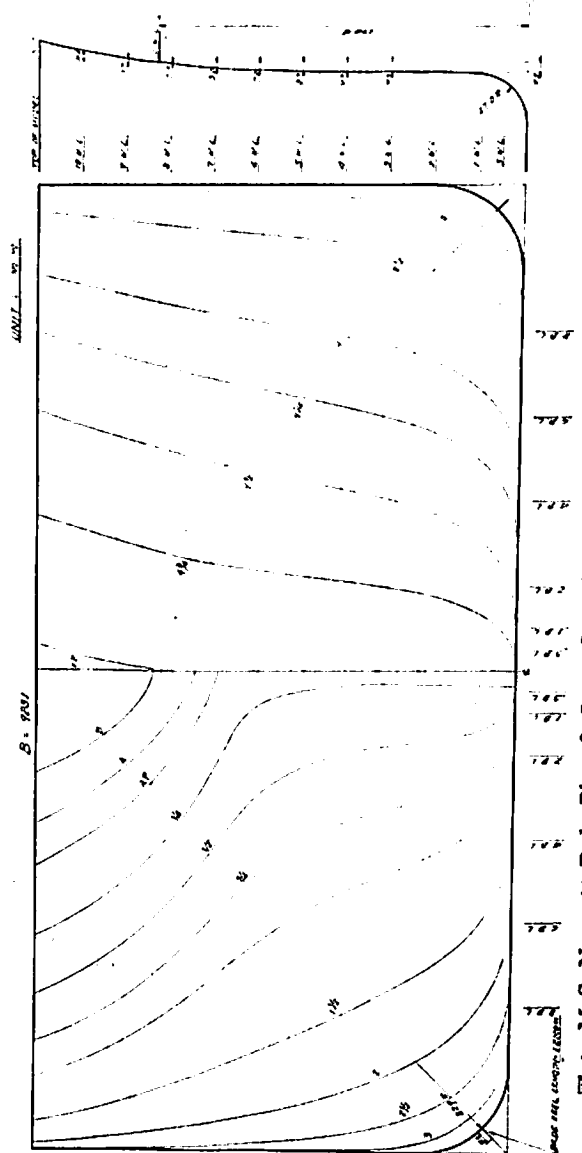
M. S. No. 1508 Body Plan & Stern, Stern Frame
